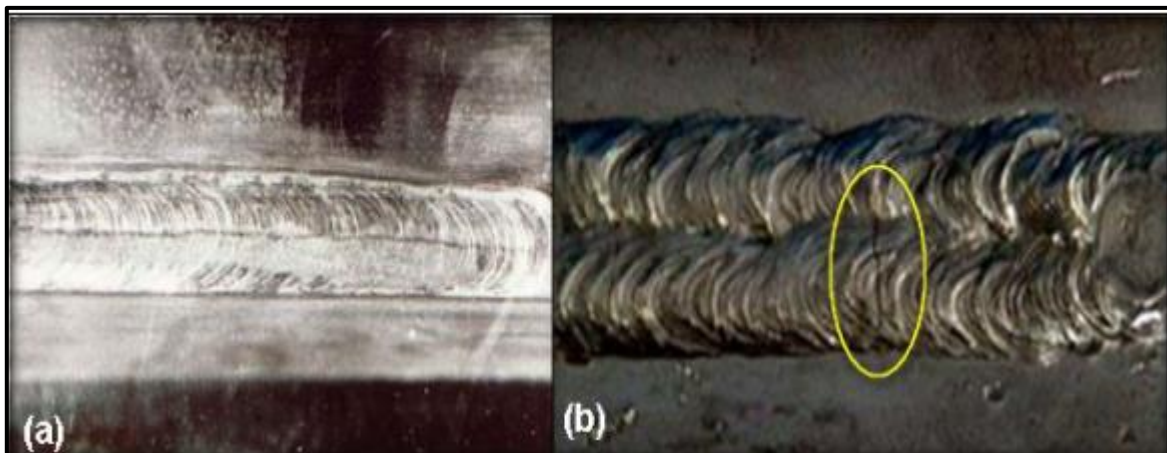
Fissure sur un cordon de soudure : (a) longitudinale, (b) Transversale [32].
